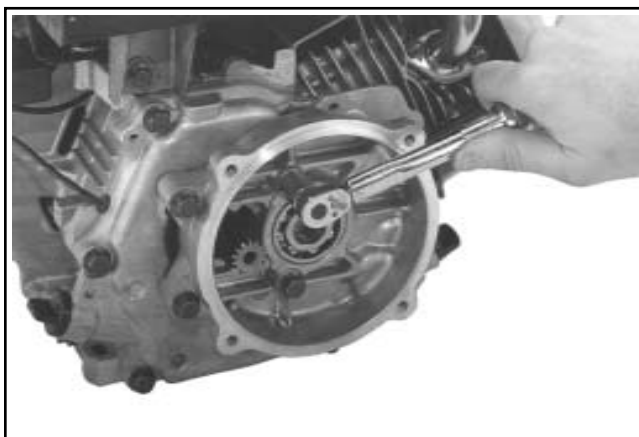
Serraggio delle viti di fissaggio della scatola.
